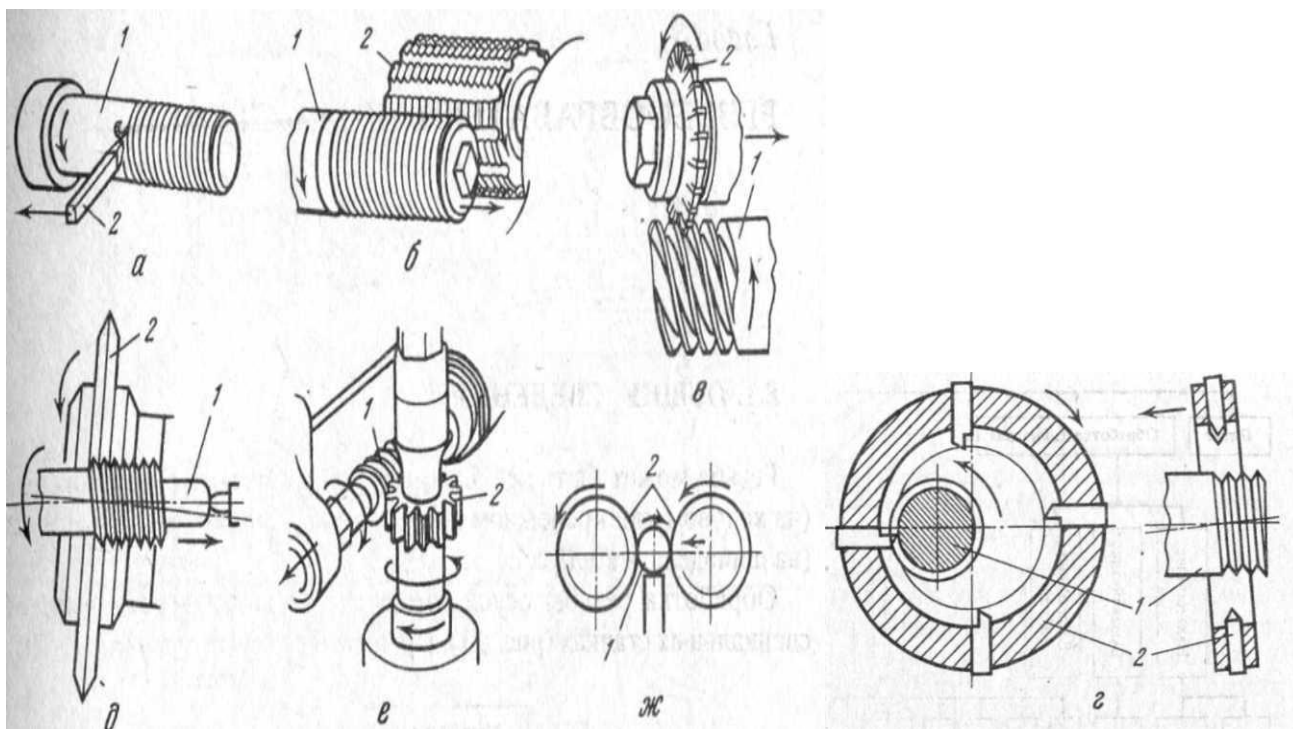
Схемы обработки резьбы: а – резцом, б – гребенчатой фрезой, в – дисковой фрезой, г – резцовой головкой, д – шлифовальным кругом, е – обкатным резцом, ж – накатными роликами, 1 – заготовка, 2 – инструмент.
